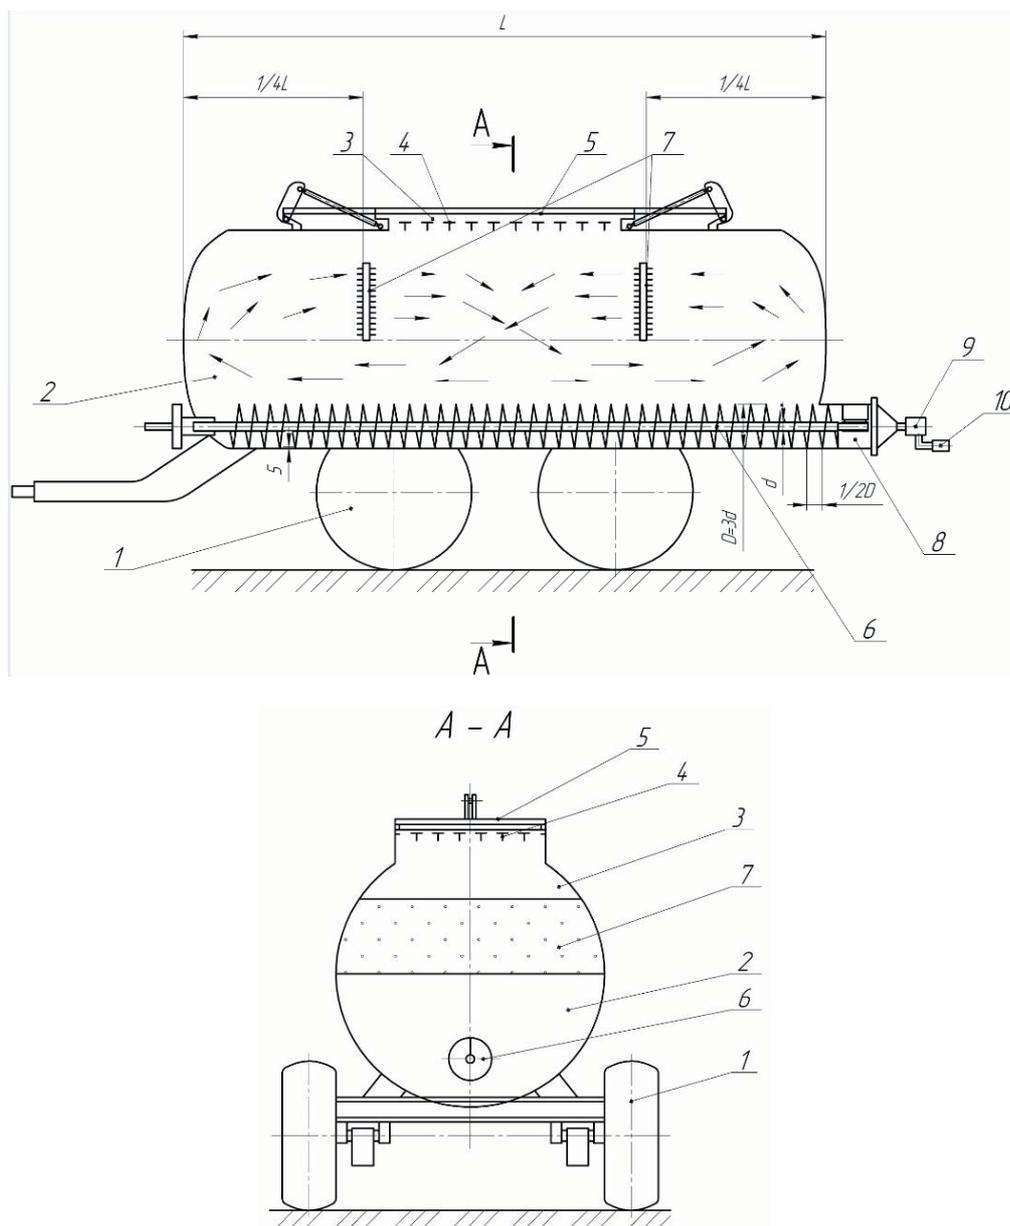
Схема общего вида мобильного узла машины для приготовления растворов жидких КОУ:
